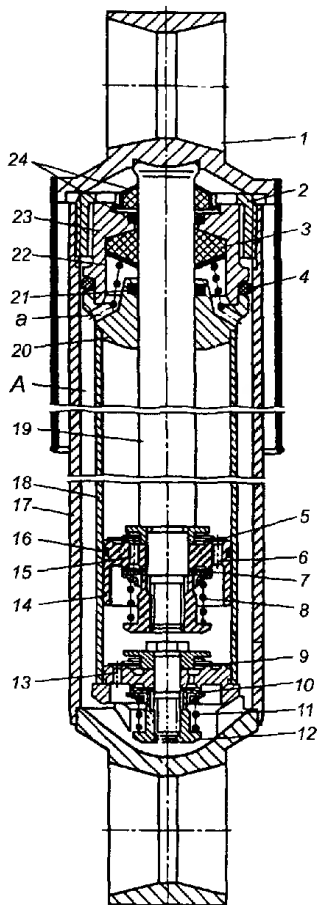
Телескопический амортизатор: 1 – проушина; 2 – гайка резервуара; 3 – уплотнительная манжета штока; 4 – уплотнительная манжета обоймы; 5 – перепускной клапан отдачи; 6 – отверстие наружного ряда; 7 – клапан отдачи; 8, 11 и 22 – пружины; 9 – перепускной клапан сжатия; 10 – клапан сжатия; 12 – гайка; 13 – отверстие перепускного клапана; 14 – поршень; 15 – отверстие внутреннего ряда; 16 – поршневое кольцо; 17 – корпус резервуара; 18 – рабочий цилиндр; 19 – шток поршня; 20 – направляющая штока; 21 – уплотнительная манжета; 23 – обойма уплотнительной манжеты; 24 – войлочные уплотнительные манжеты штока; а – отверстие для слива жидкости в резервуар; А – полость резервуара.
